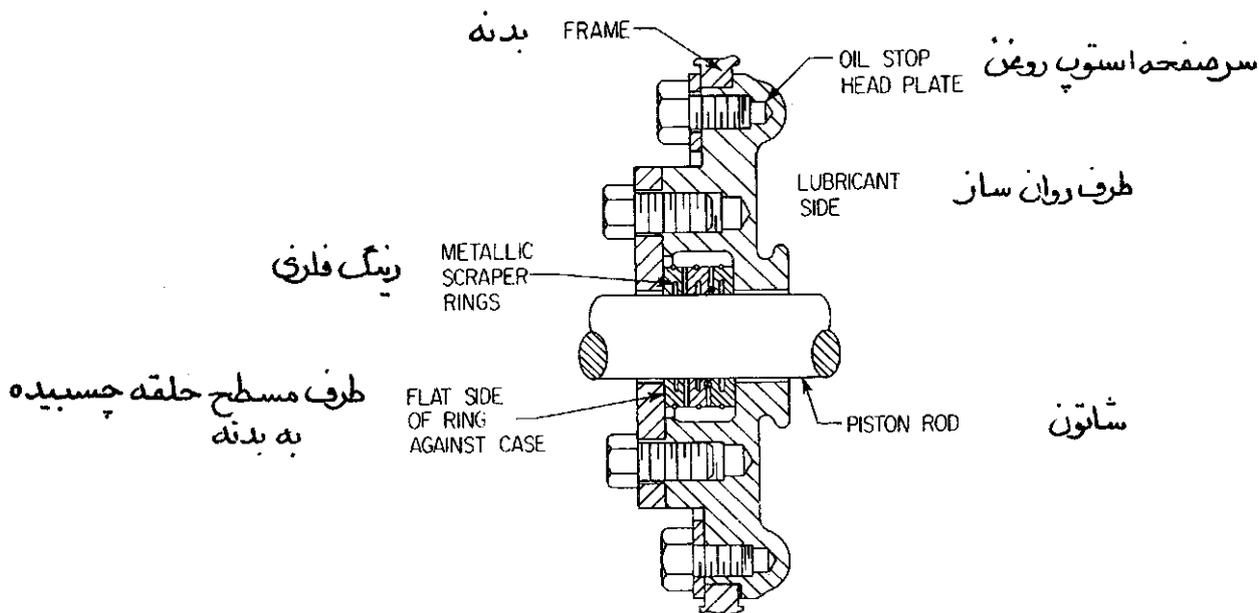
Oil-stop-head packing شکل ۵-۸ واشر مانع عبور روغن
